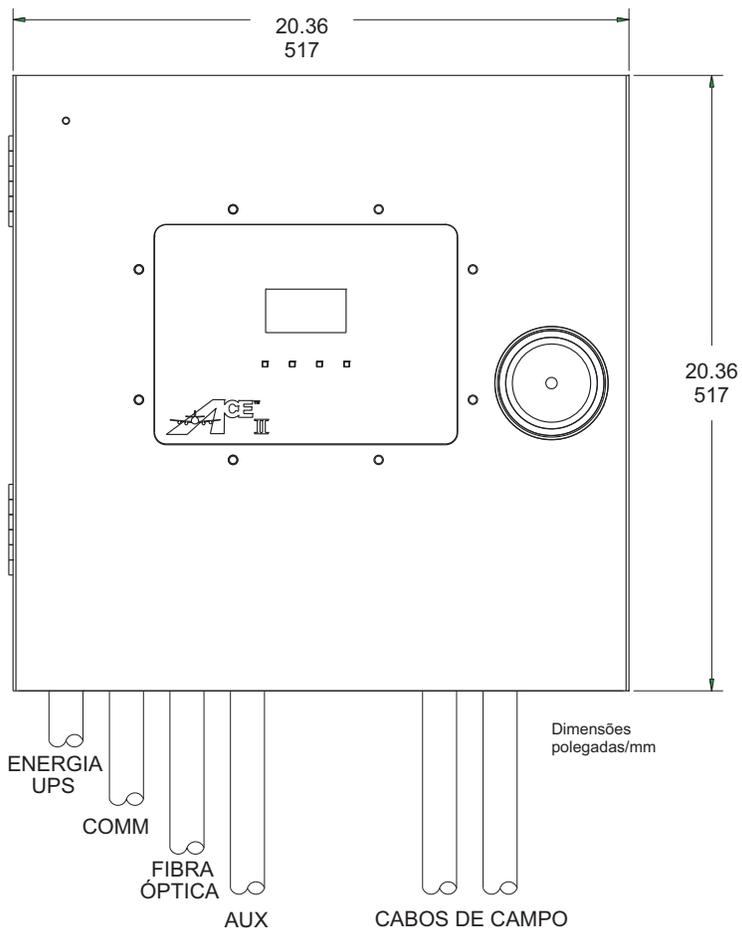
Suporte de Caixa Combinada, Detalhe da parte superior
